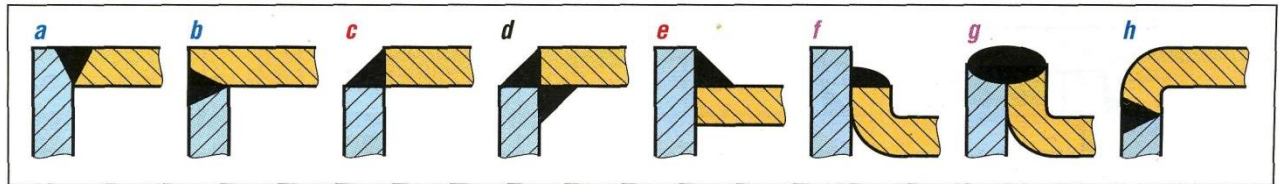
soudures en angle ou en L. Pour d soudage des deux côtés.
